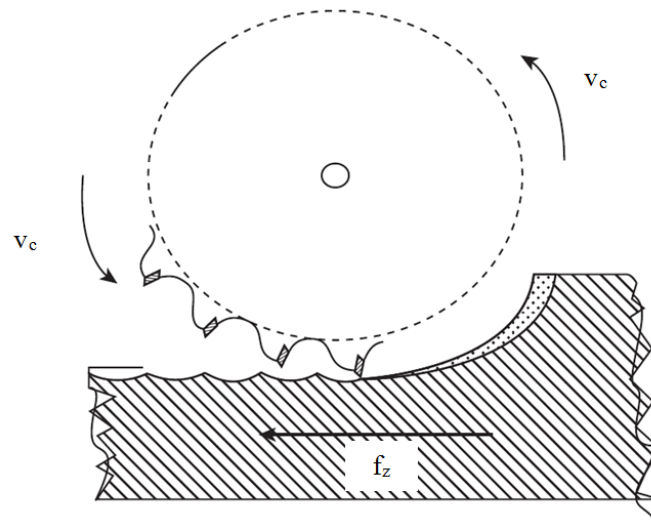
Formação do cavaco durante o serramento circular discordante
